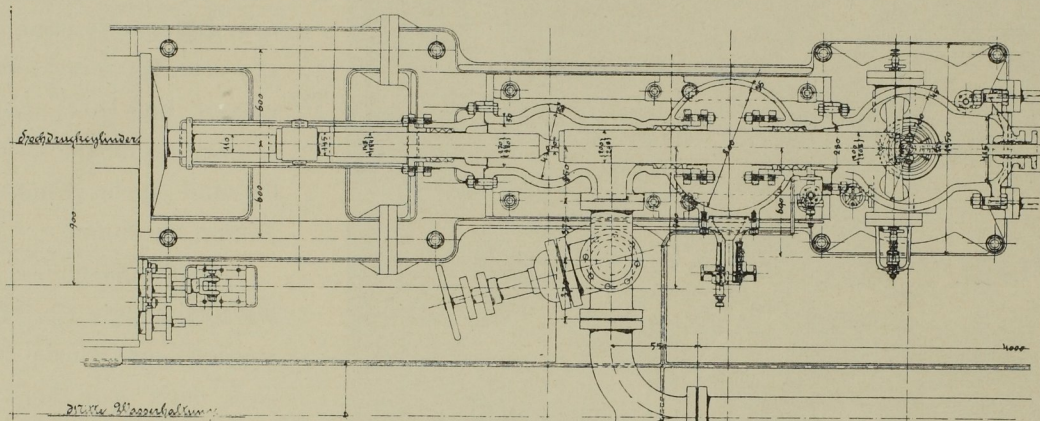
Grundriss der Pumpe. Masst. 1:45.
